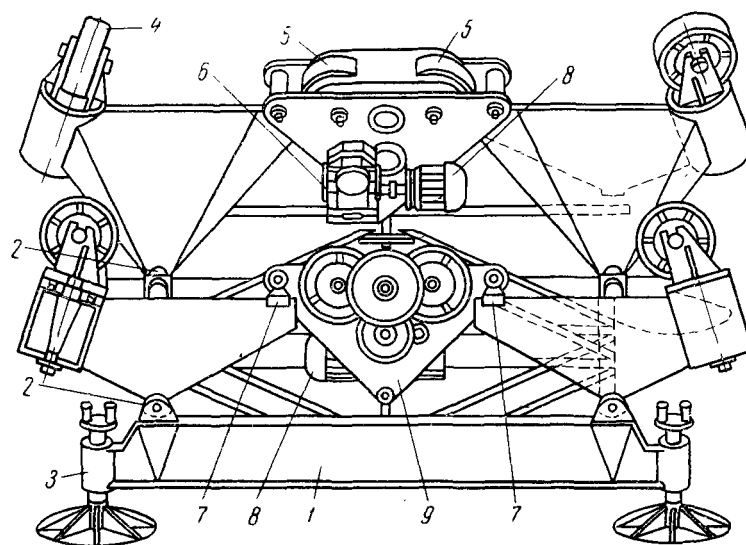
Манипулятор для вращения сферического резервуара при сварке
